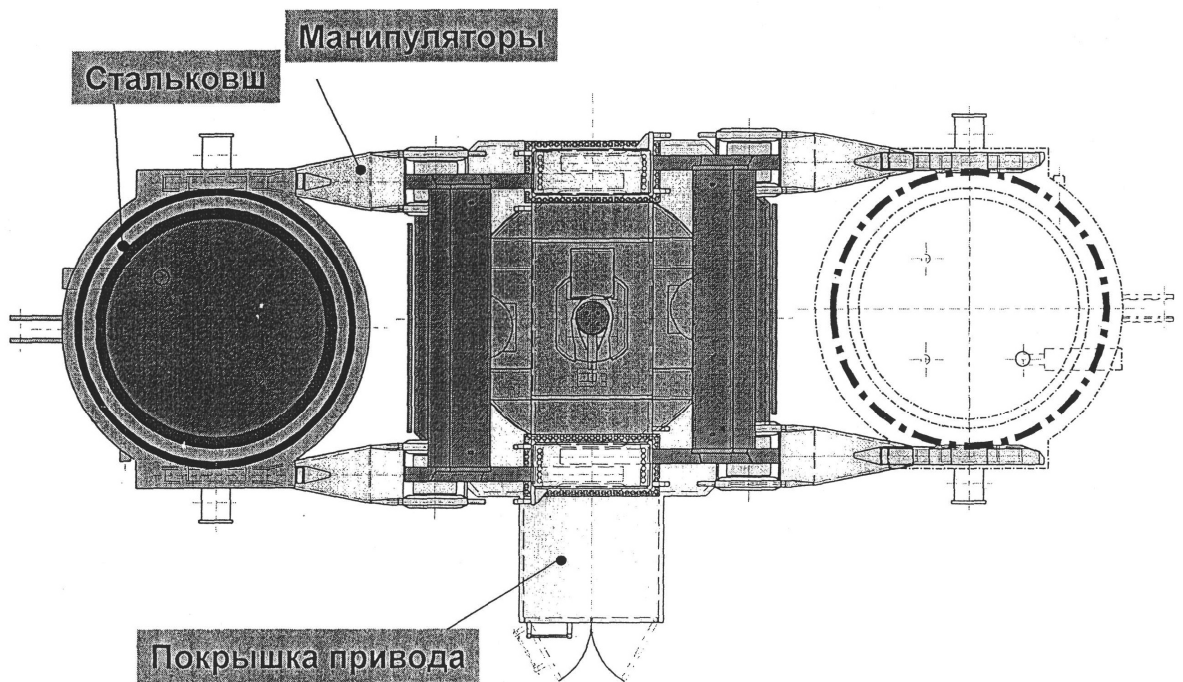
Підйомно–обертальний стенд (вид зверху)
